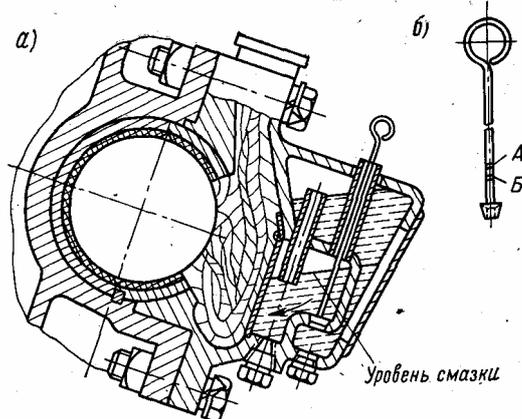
Узел моторно-осевого подшипника (а) и специальный указатель уровня смазки (б)
